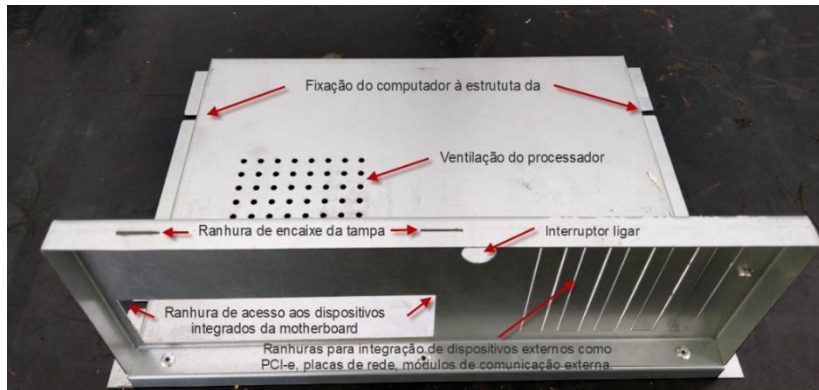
Detalhes técnicos de montagem da caixa do computador
